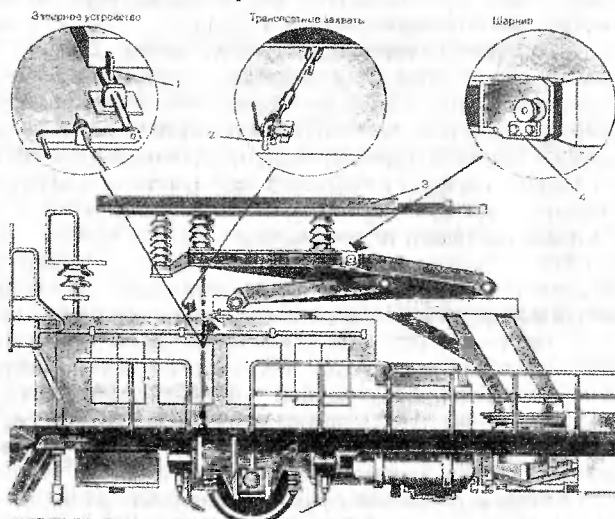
Механизм подъема рабочей площадки автомотрисы АДМ:
